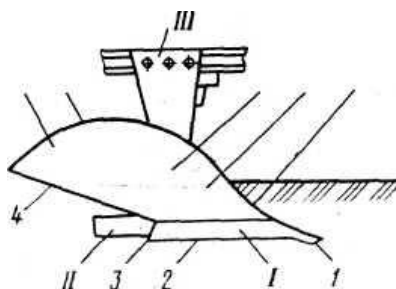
Лемешно-отвальный плужный корпус: I – лемех; II – полевая доска; III – стойка; IV – отвал; 1 – носок лемеха; 2 – лезвие; 3 – пятка; 4, 6 и 8 – соответственно бороздной, верхней и полевой обреза; 5 – крыло; 7 – грудь отвала
